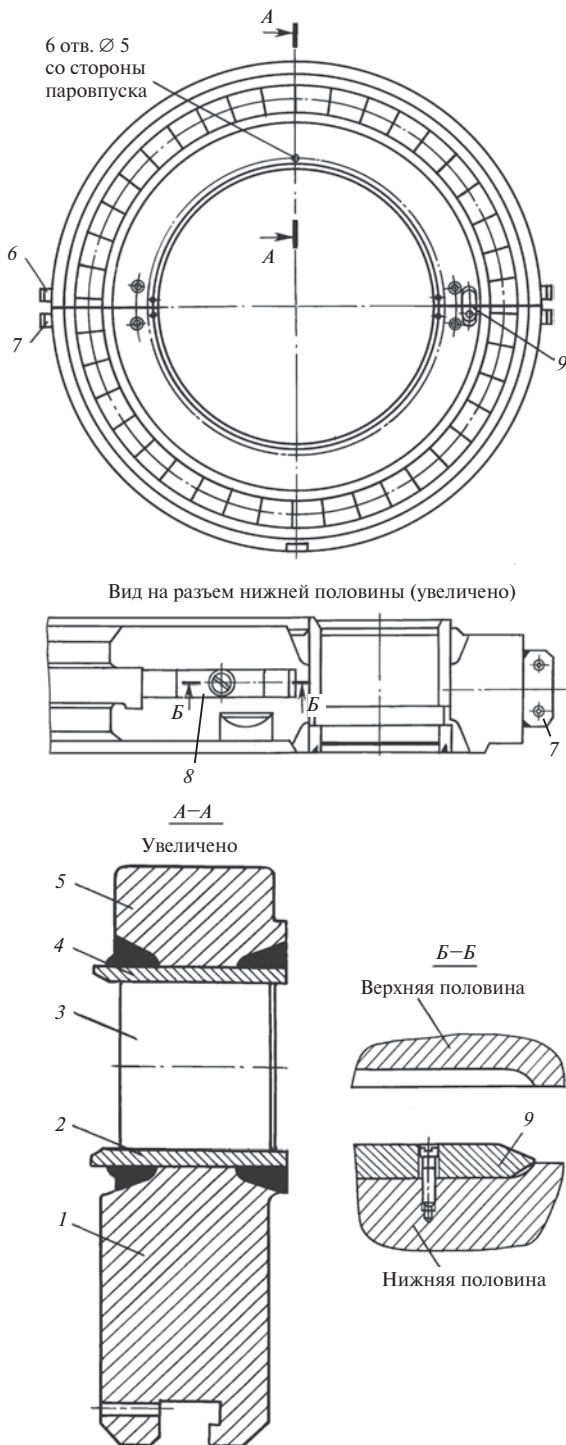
Сварная диафрагма для ЦВД турбин
